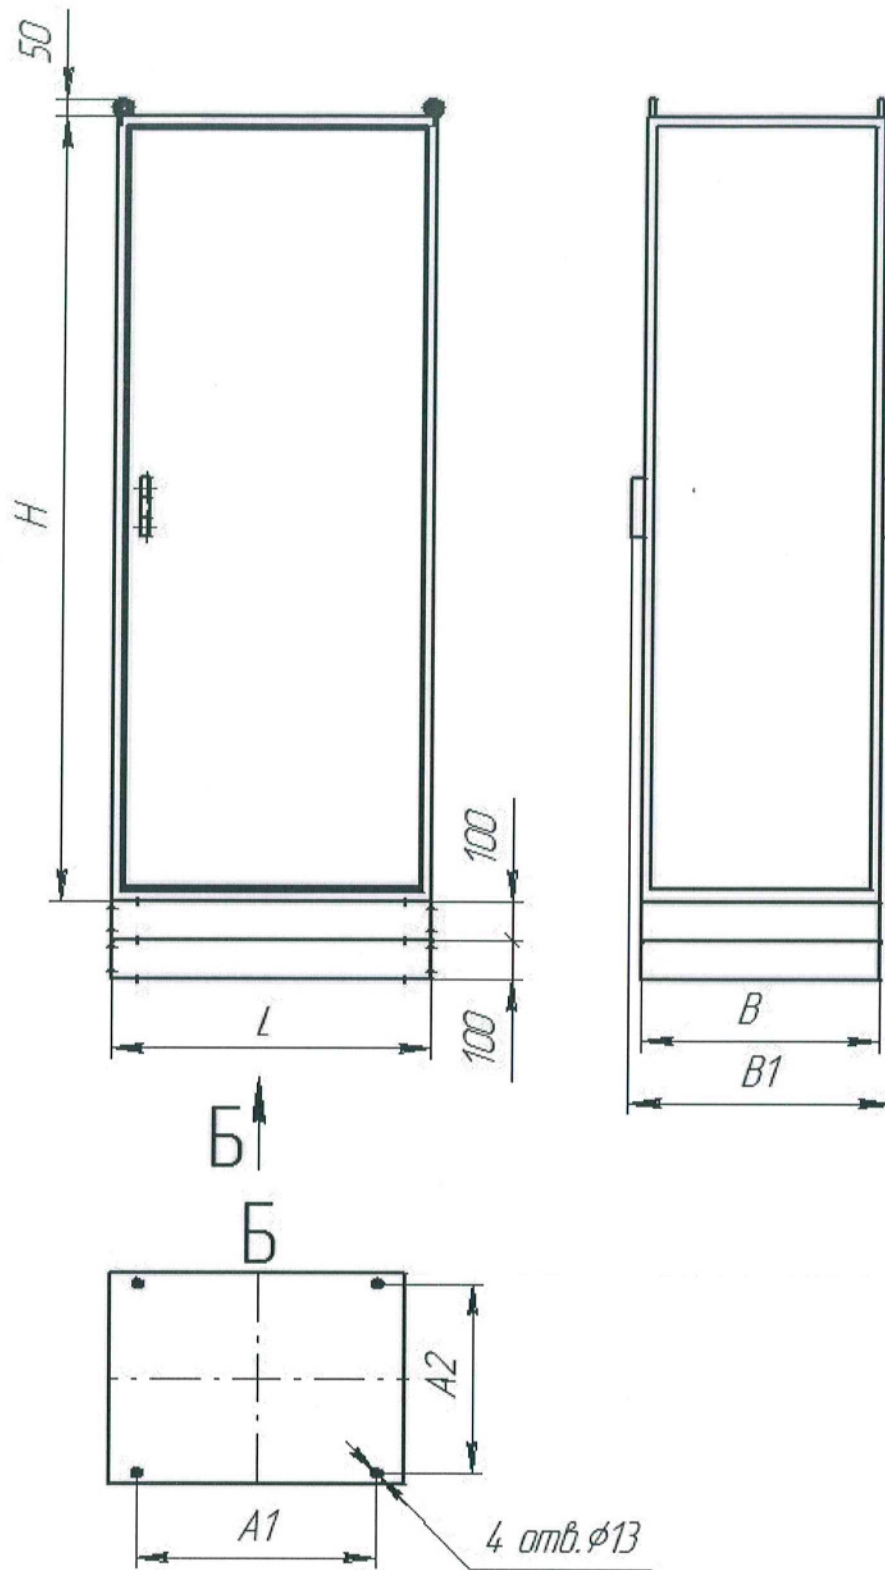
Габаритные и установочные размеры шкафа с двумя цоколями
